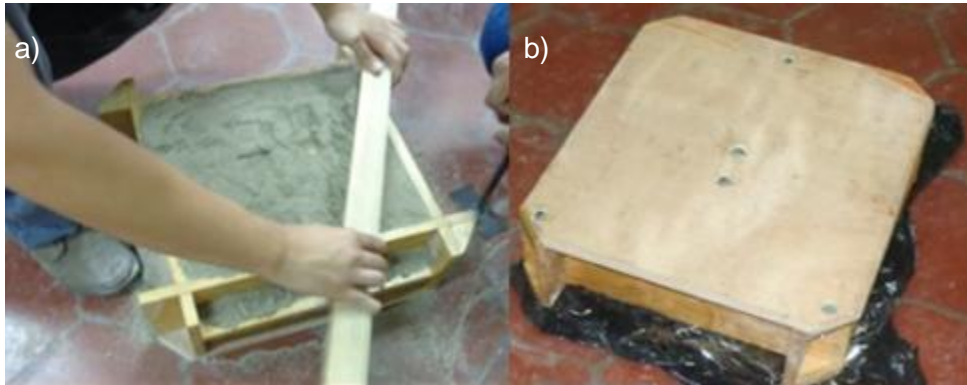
Forma para remover el exceso de arena y giro de la caja de moldeo.
